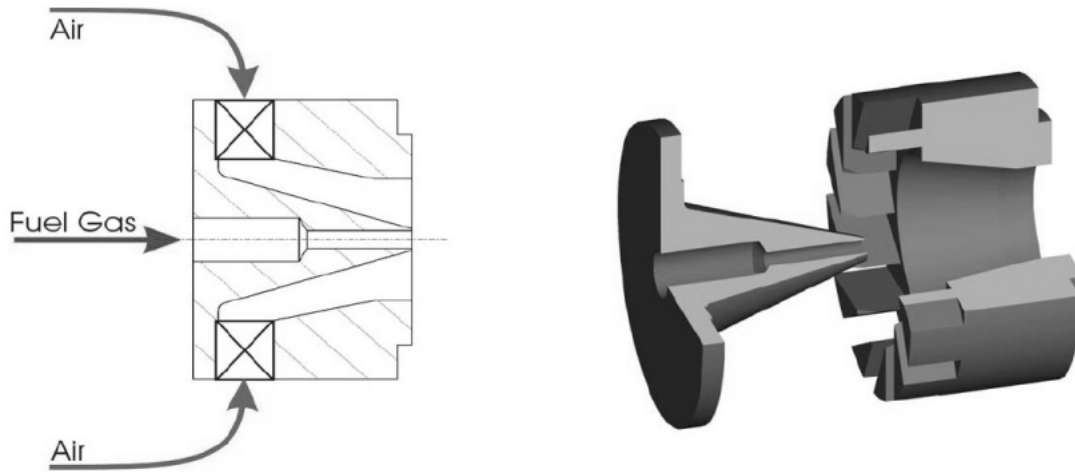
Schemata (links) und Explosionszeichnung (rechts) des Drallbrenners.
